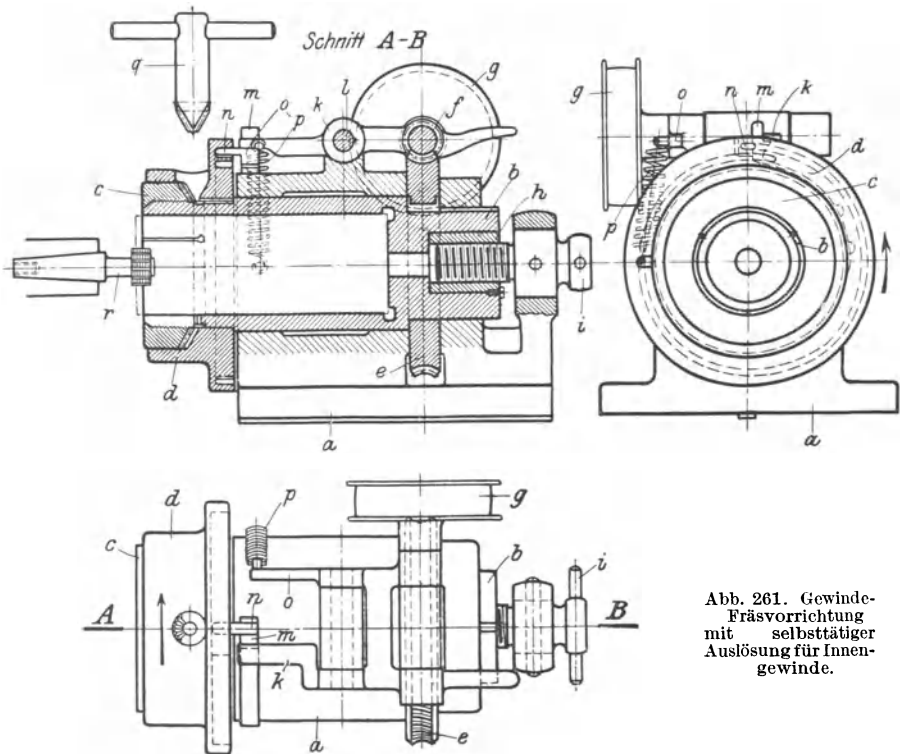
Gewinde-Fräsvorrichtung mit selbsttätiger Auslösung für Innengewinde.
